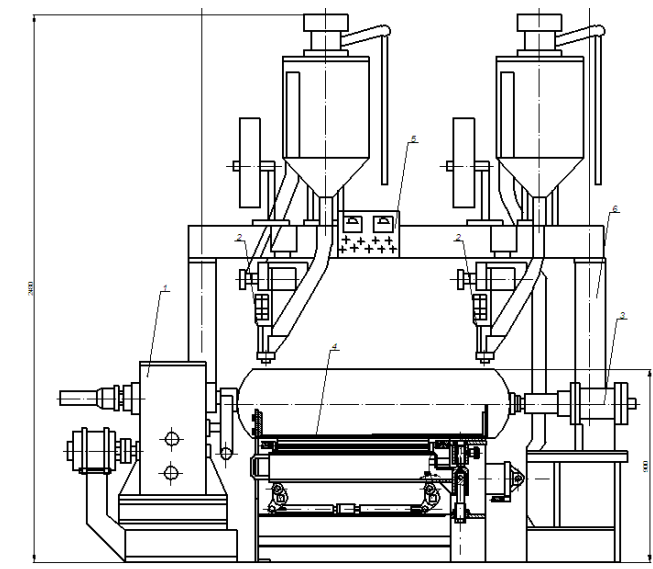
Загальний вигляд спеціалізованої зварювальної установки Р-879
